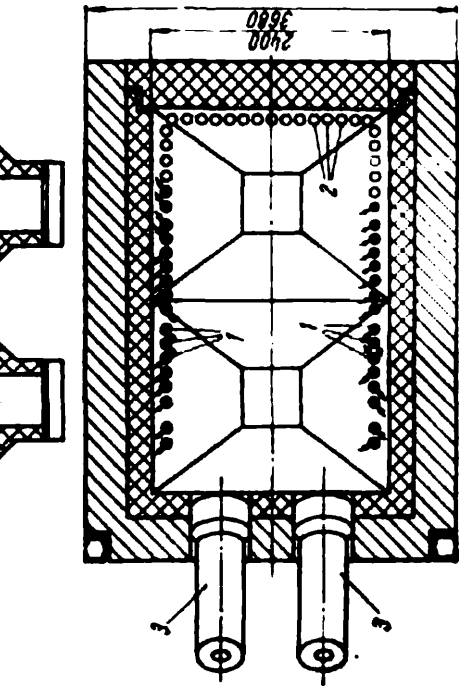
Размещение горелки в месте нахождения сварных труб гонки.
